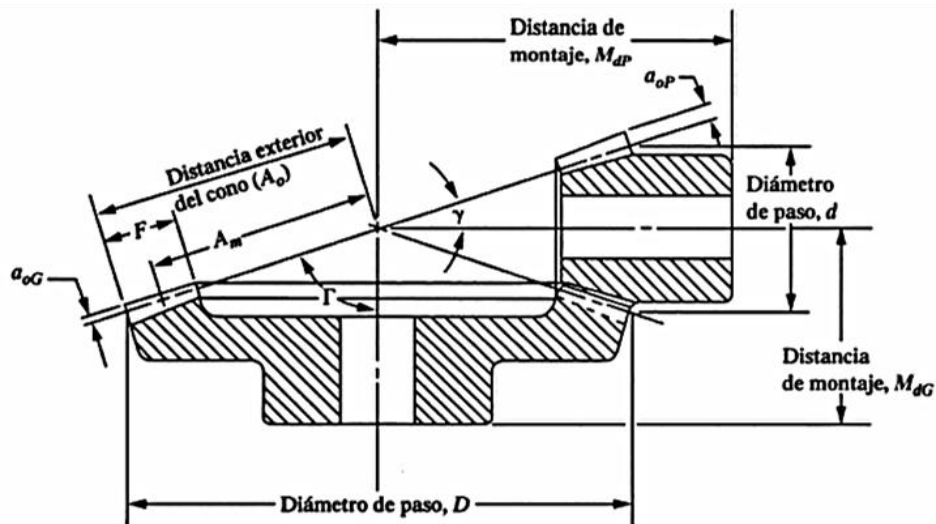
Dimensiones principales de dos engranes cónicos con dientes rectos.
